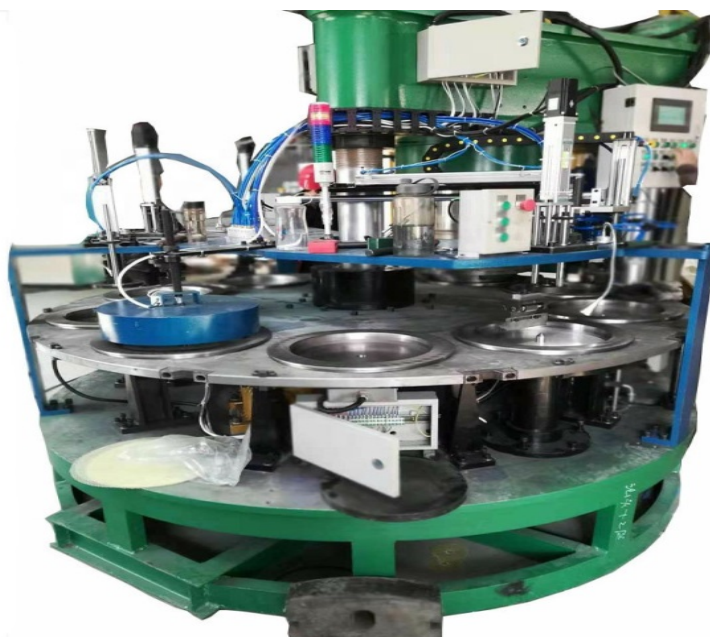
Восьмиступенчатый автоматический формовочный пресс с вращающейся прессформой
